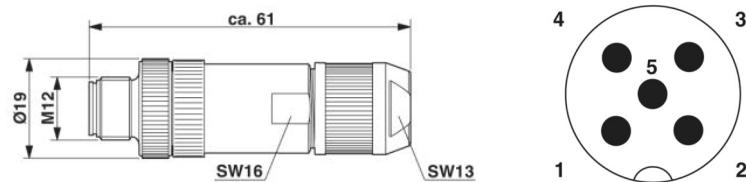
Stecker M12 x 1 gerade, geschirmt ; Polbild Stecker M12, 5-polig, A-kodiert, Ansicht Stiftseite, Phoenix Bezeichnung: SACC-M12MS-5SC SH
